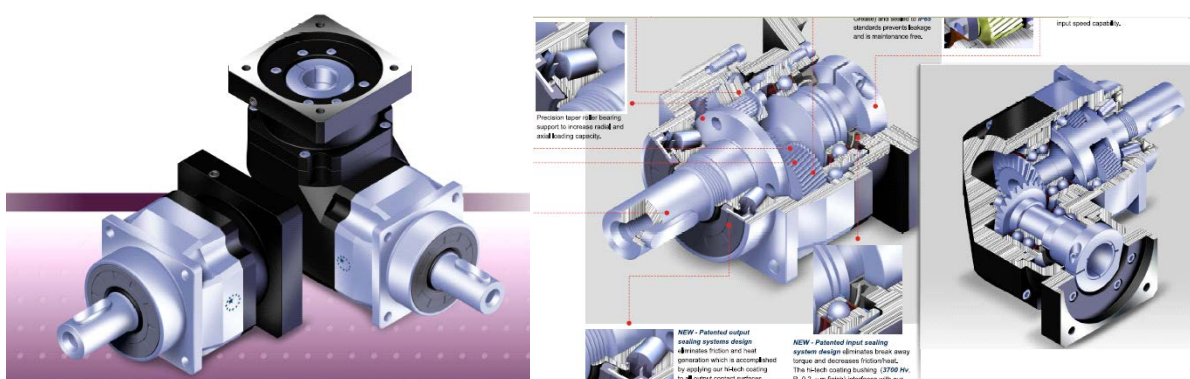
Общий вид и устройство редукторов Apex Dynamics
